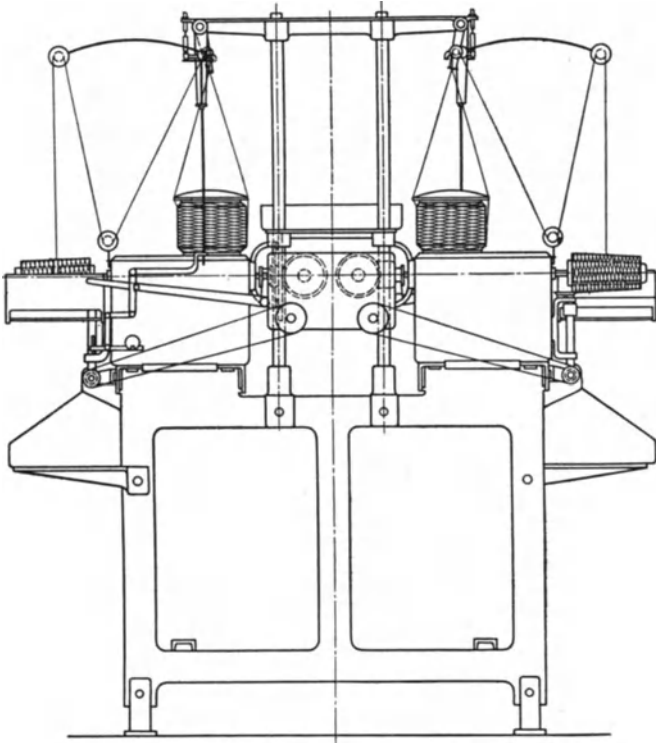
Präzisionskreuzspulmaschine mit Ablaufzeug für Spinnkuchen oder Zwirnwinkel.
